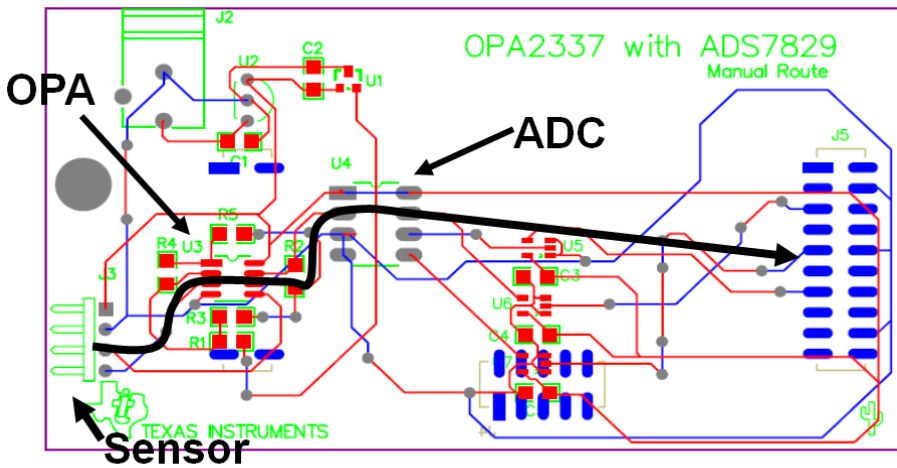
考虑到噪声抑制后的 PCB 布局布线
